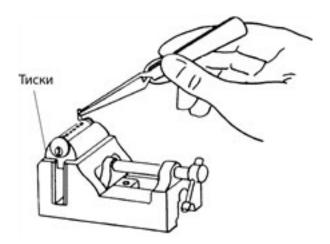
Извлеките штырь заглушки цилиндра и, провернув против часовой стрелки, вытащите ее (диаметр цилиндра 5/8 дюйма = 16 мм) (С разрешения компании Schlage Lock Company)
